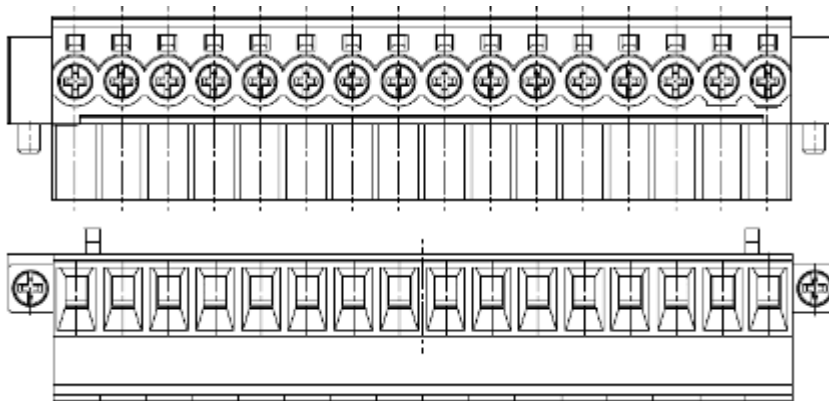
16-polige Prozessklemme (Schrankaufbau)
